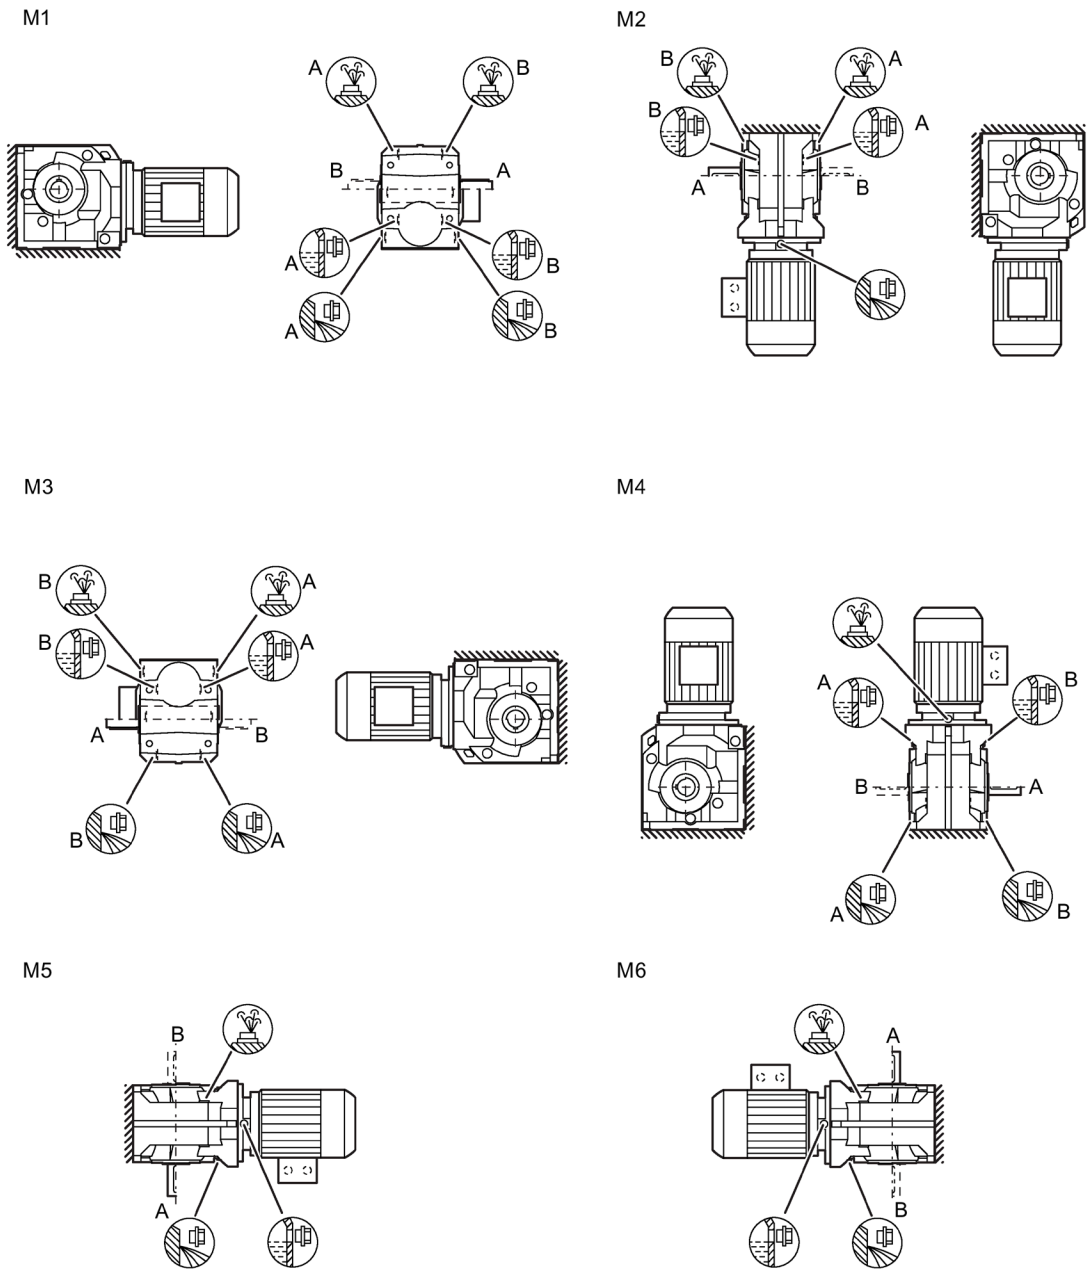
Einbaulagen für Stirradschneckengetriebe C. Fußausführung Baugrößen 39 - 89
